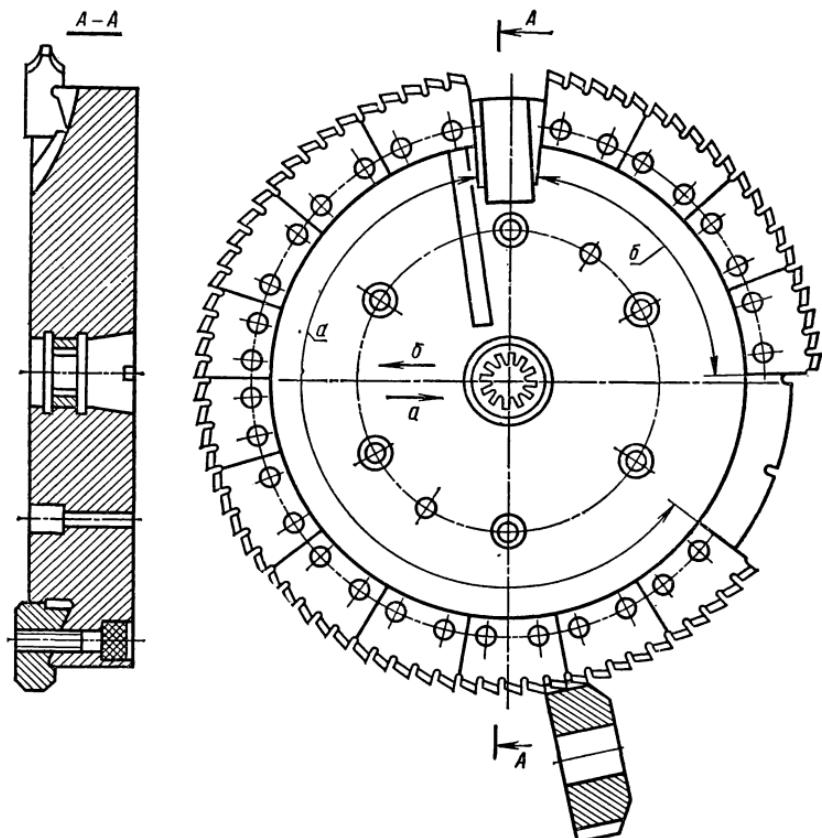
Круговая протяжка для нарезания зубьев конических зубчатых колес:
